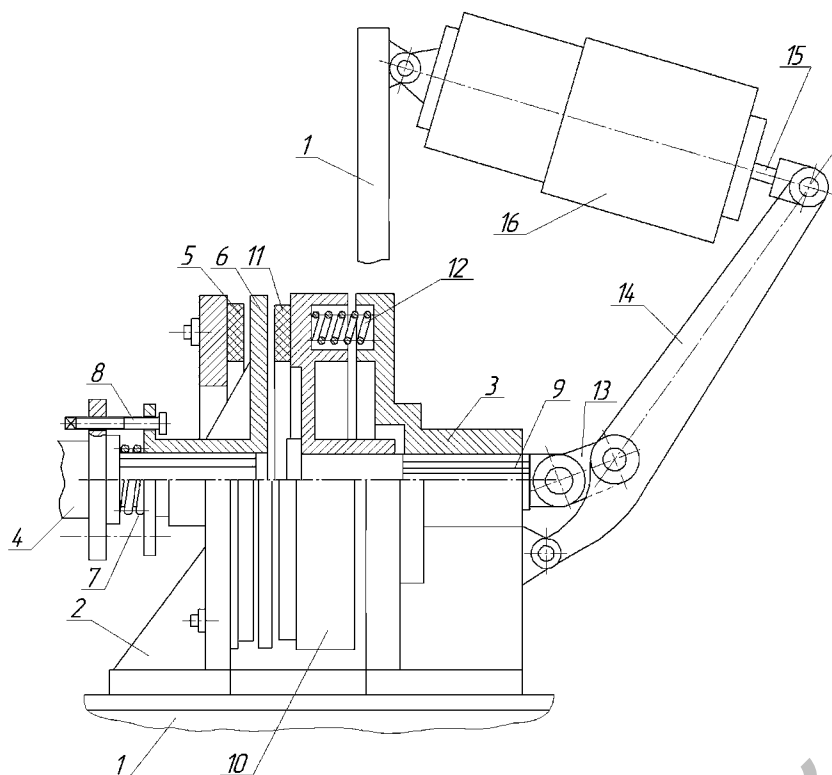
Дисково-колодочный тормоз ленточного конвейера
